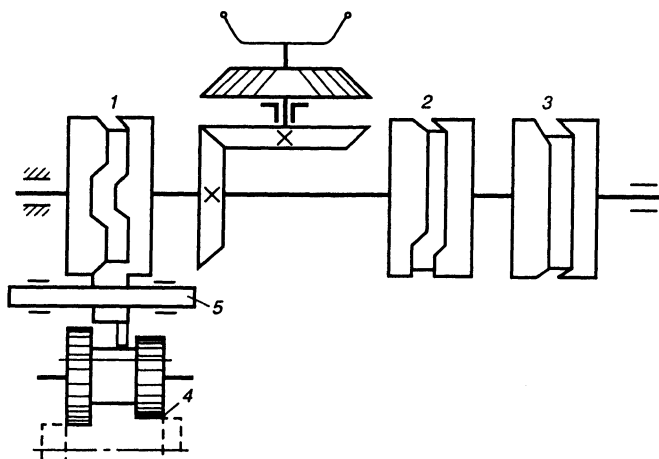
Схема устройства с однорукояточным управлением для перемещения зубчатых колес
